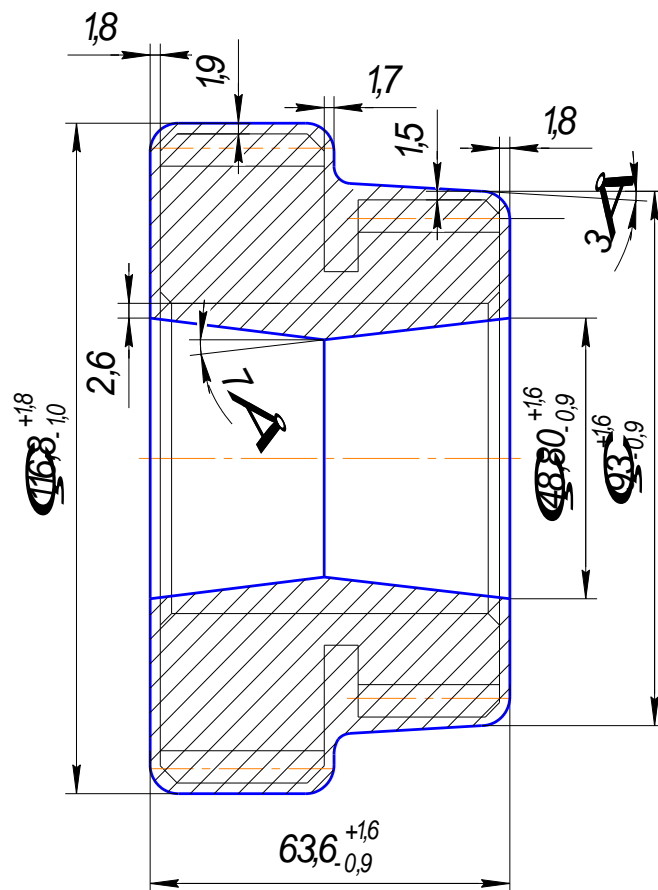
Заготовка сателіту з нарахованими припусками та допусками
